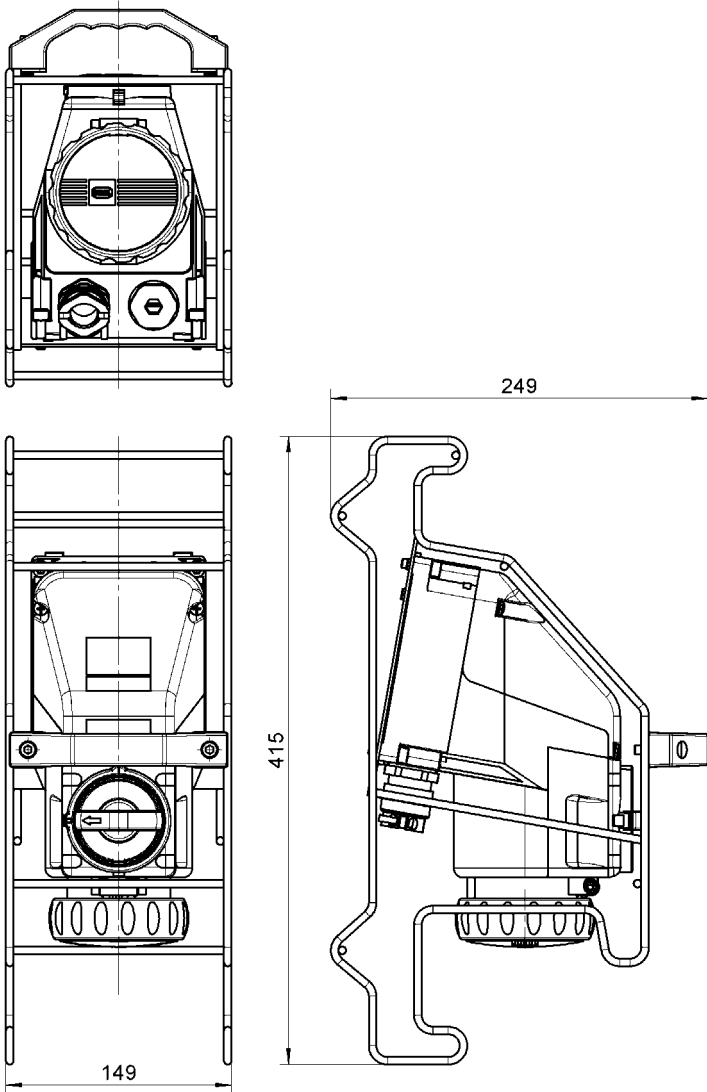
Maßzeichnung Typ 8570/16..
